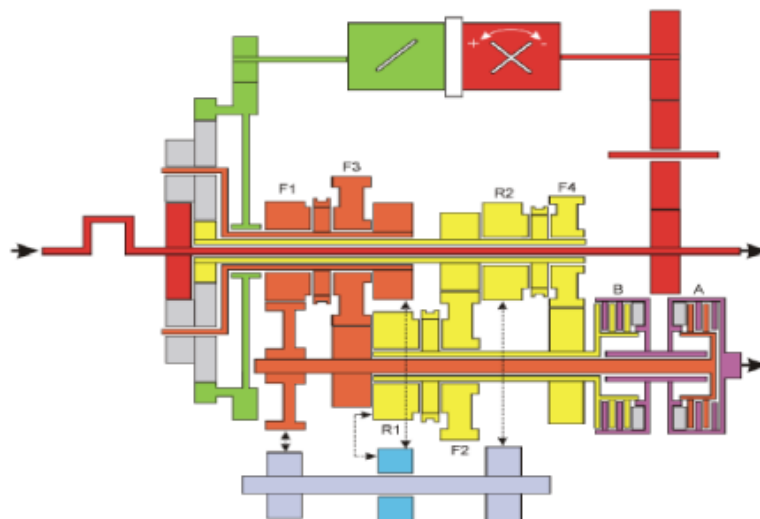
Slučovací planetový převod, zdroj:
